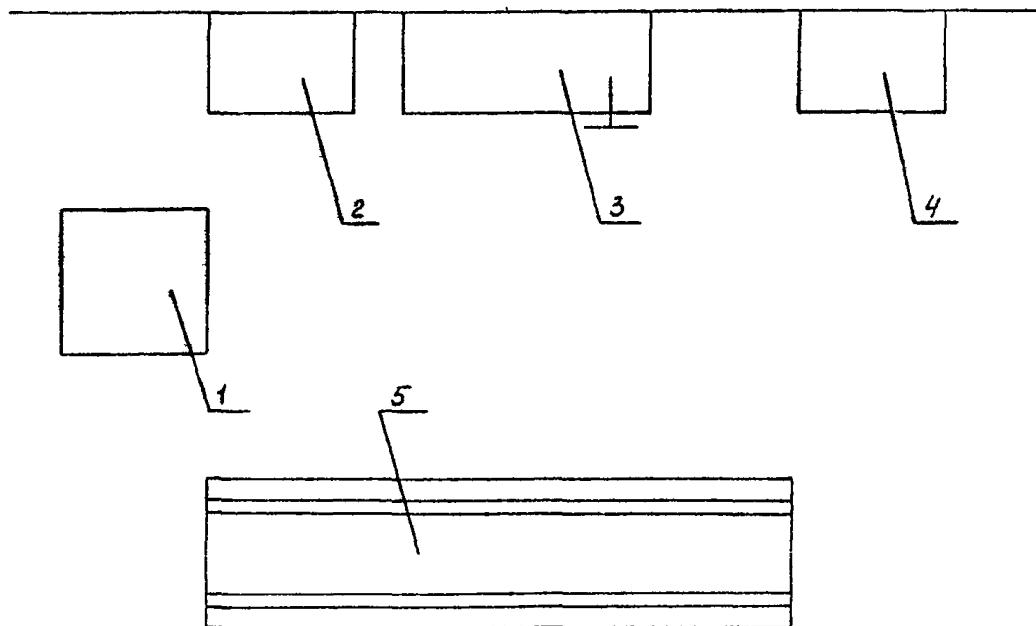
Рис. II. Типовая схема планировки рабочего места сборки передней оси
